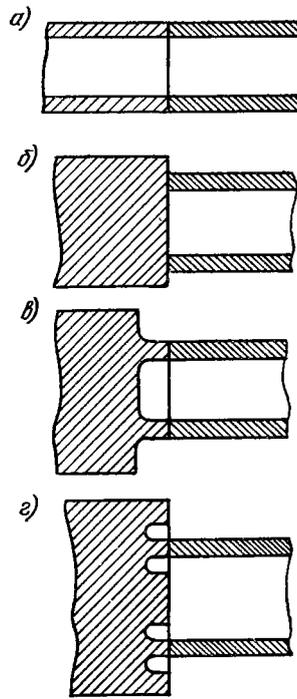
Образцы подготовки к стыковой сварке трубчатых соединений
